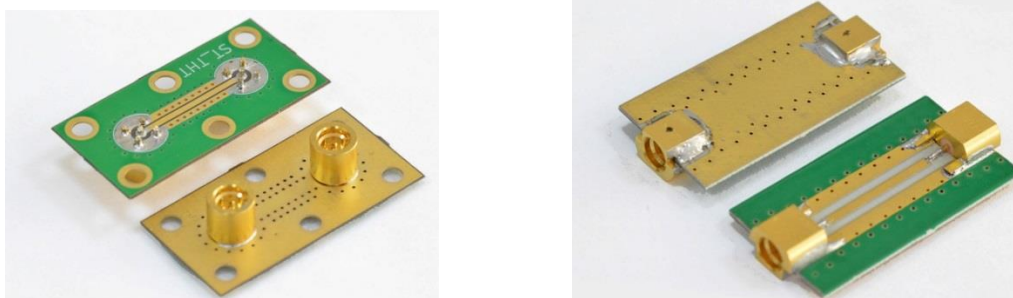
Внешний вид печатных плат с установленными соединителями:
